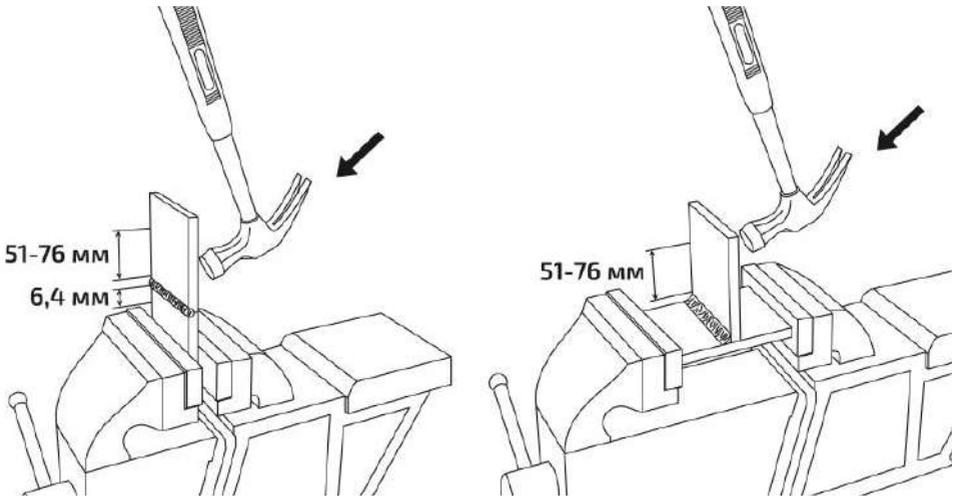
Проверка на прочность сварного соединения.
